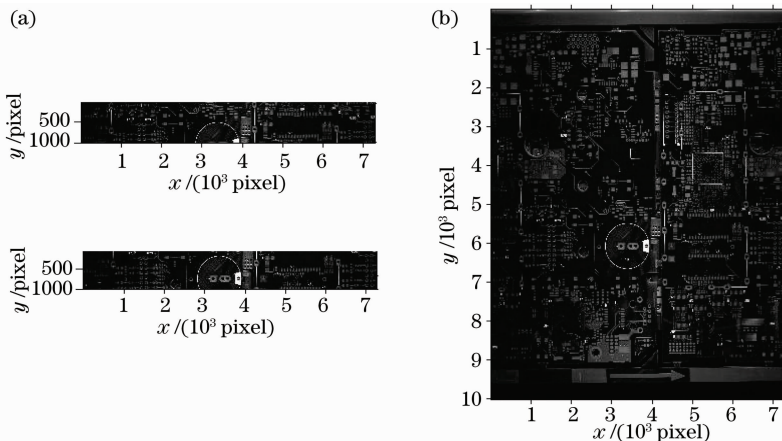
获取的 PCB 光电图像。(a) 相邻局部图像, (b) 全景 PCB 光电图像
